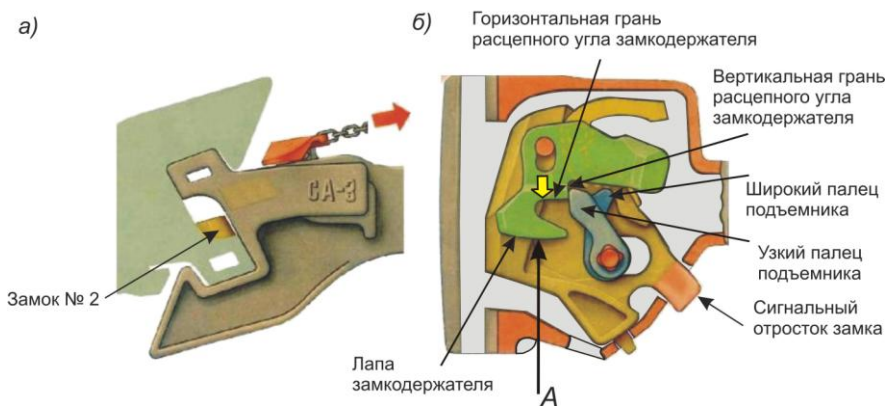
Положения деталей механизма автосцепок при расцеплении (этап III):
